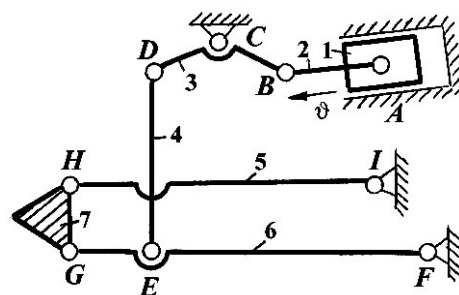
Гидрорычажный механизм тракторного навесного устройства
